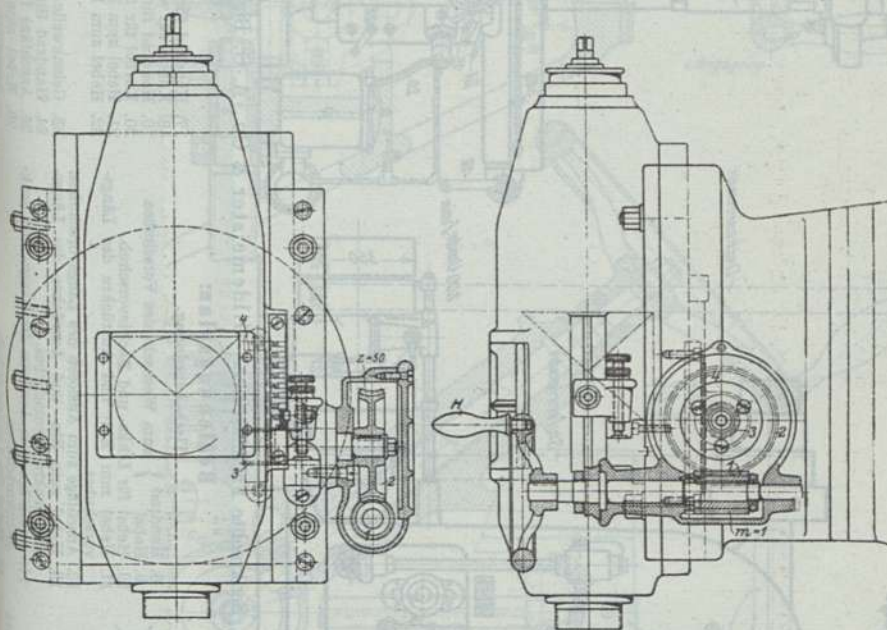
und 572. Einstellvorrichtung des Frässchlittens.
